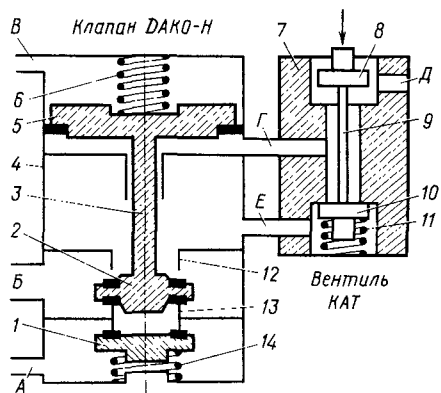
Схема работы клапана ДАКО-Н: 1 — ограничительный клапан; 2 — рабочий клапан; 3 — шток; 4 — корпус клапана; 5 — поршень; 6, 11, 14 — пружины; 7 — корпус вентиля; 8, 10 — выпускной и впускной клапаны; 9 — игла; 12, 13 — наполнительное и выпускное седла; А, Б, В, Г, Е — каналы; Д — отверстие
